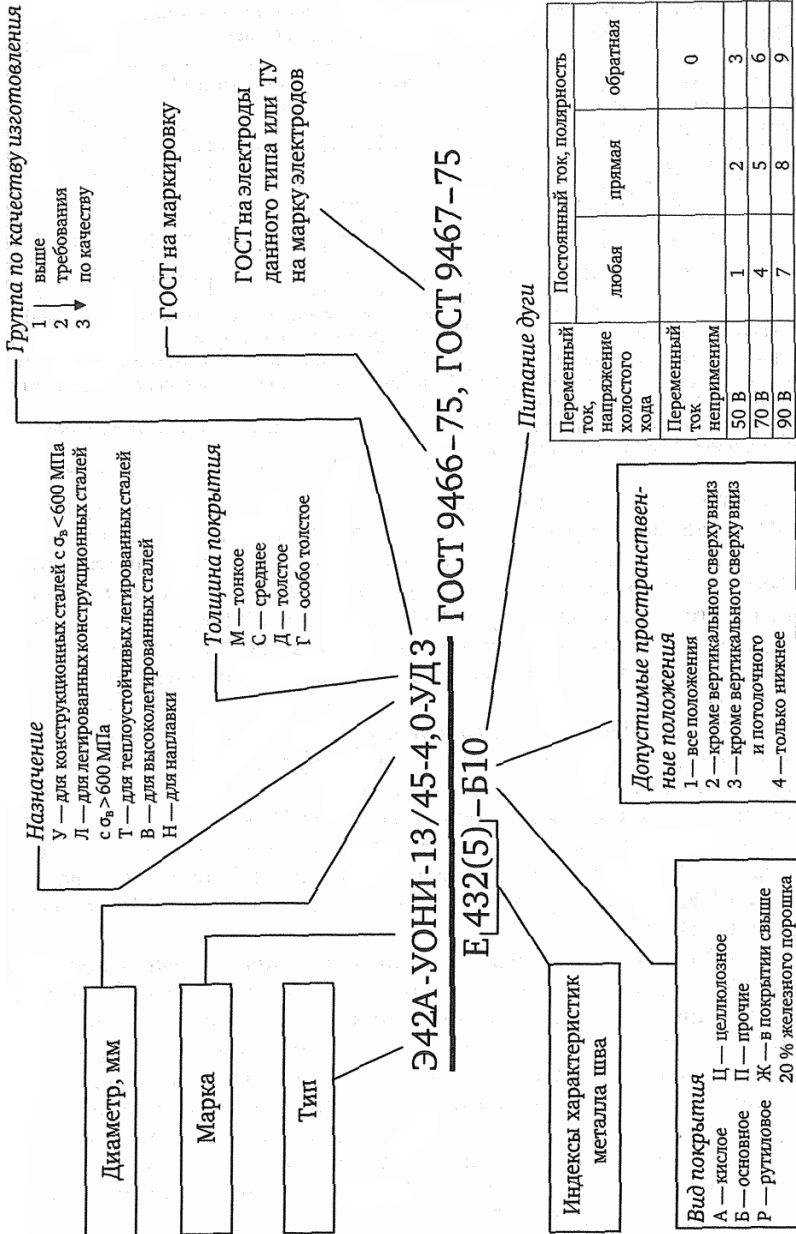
Условные обозначения покрытых электродов для сварки и наплавки стали (по ГОСТ 9466-75)
